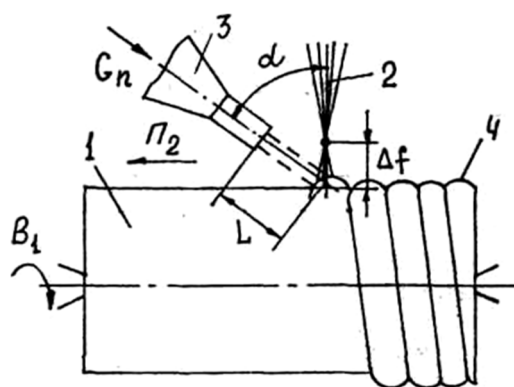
Схема газоплазменной лазерной наплавки
